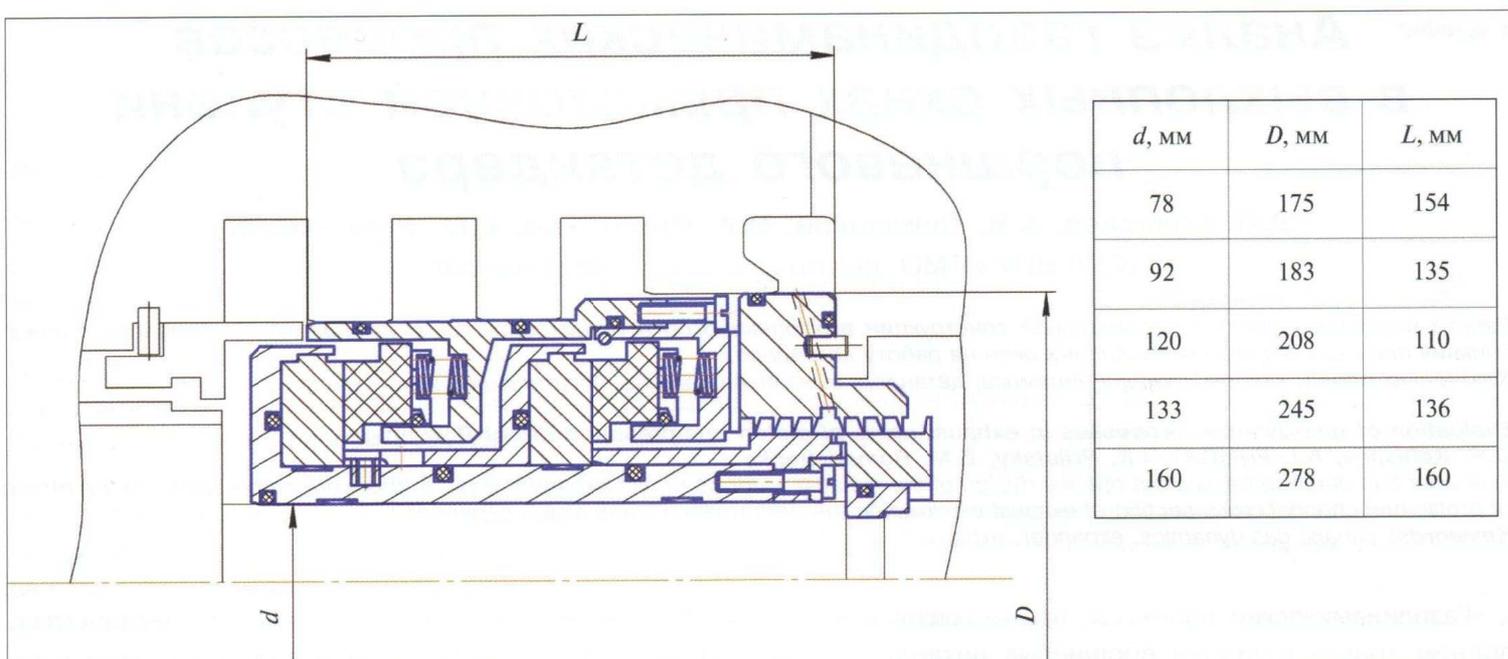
Типоразмерный ряд СГУ, разработки ЗАО НТК для ЦК
